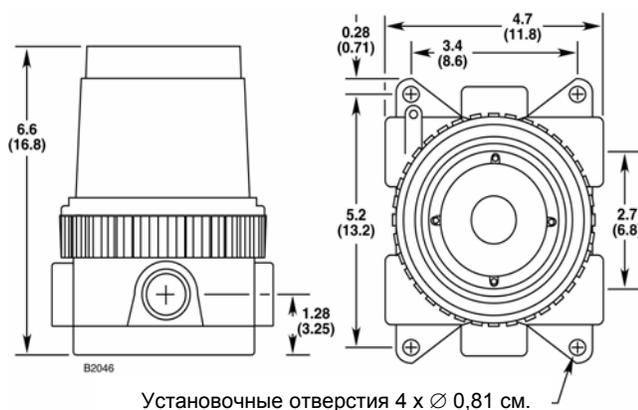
Габаритные размеры коробки соединительной с высокой крышкой в дюймах (см).
